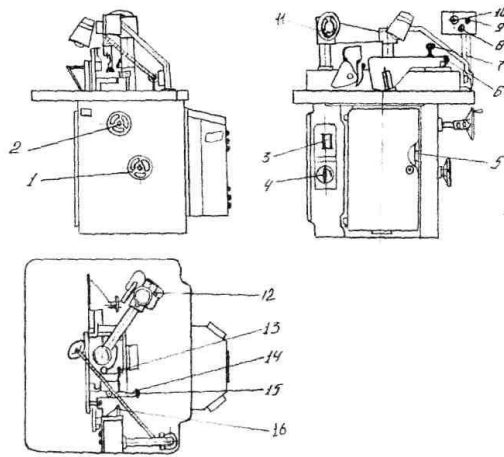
Загальний вигляд верстата ФС: 1 - маховичок натягування паса; 2 - маховичок переміщення бабки шпindelної; 3 - автомат ввідний; 4 - перемикач вибору швидкості шпindelя; 5 - рукоятка фіксації шпindelної бабки; 6 - кнопка фіксації щитка захисту інструменту; 7 - кнопка обмеження ходу щитка захисту інструменту; 8 - арматура сигнальна; 9 - кнопка управління "Пуск верстату"; 10 - кнопка управління "Стоп верстату"; 11 - маховичок переміщення кронштейна шпindelя; 12 - ручка фіксації кронштейна шпindelя; 13 - ручка фіксації корпусу огороження інструменту; 14 - кнопка фіксації кронштейна лінійки; 15 - кнопка переміщення кронштейна лінійки; 16 - рукоятка фіксації лінійки
